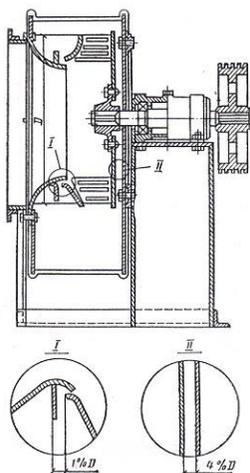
Проверка зазоров между диском рабочего колеса и кромкой входного патрубка вентилятора
